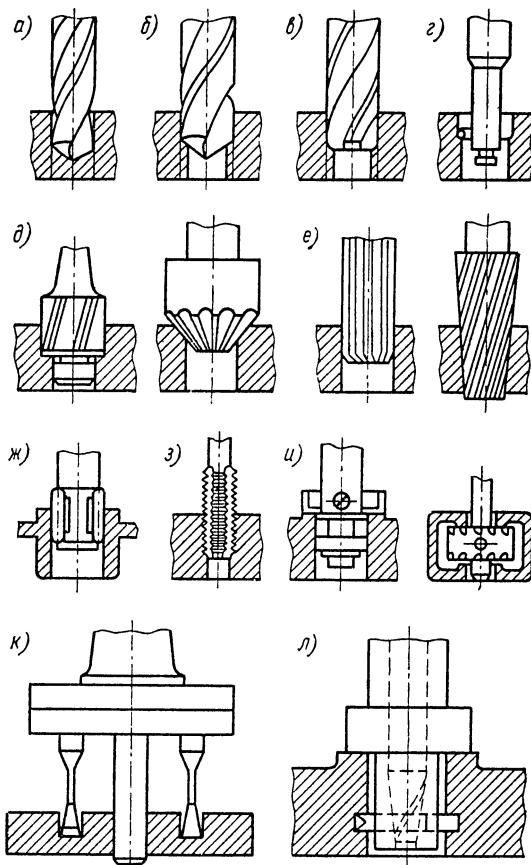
Типовые переходы при обработке отверстий и их элементов: а — сверление; б — рассверливание; в — зенкерование; г — растачивание; д — зенкование; е — развертывание; ж — выглаживание; з — нарезание внутренней резьбы; и — цекование (подрезка) торцов; к — вырезание дисков (шайб); л — проточка внутренних канавок
